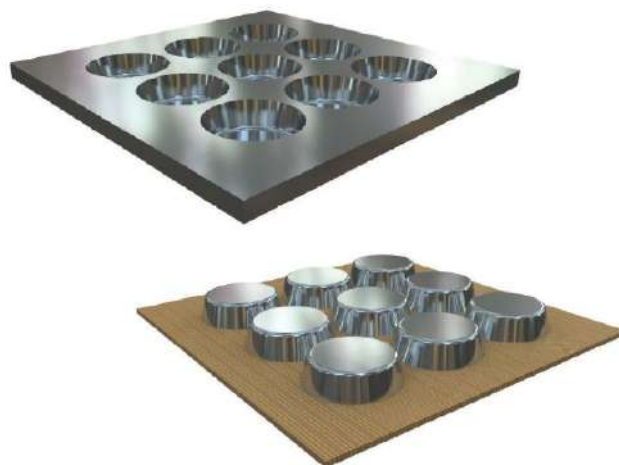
Exemplo de molde macho e fêmea do Vacuum Forming.
